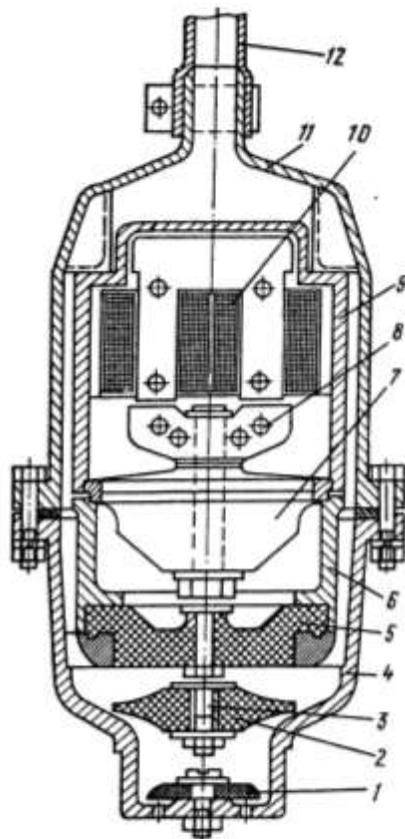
Конструкция вибрационного насоса НЭБ-1/20 с погружным вибратором: 1 — приемный клапан; 2 — рабочий орган — поршень; 3 — шток; 4, 6, 9, 11 — детали корпуса; 5 — диафрагма; 7 — амортизатор; 8 — якорь; 10 — катушки электромагнита; 12 — напорный шланг
